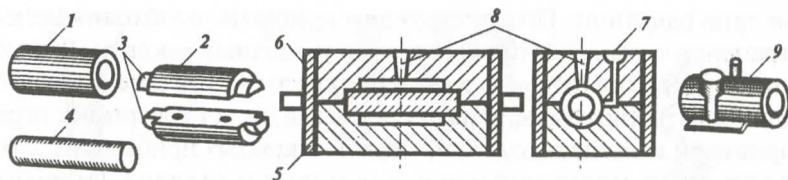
Отливка детали в разовой форме. Литейная форма из формовочной смеси:
